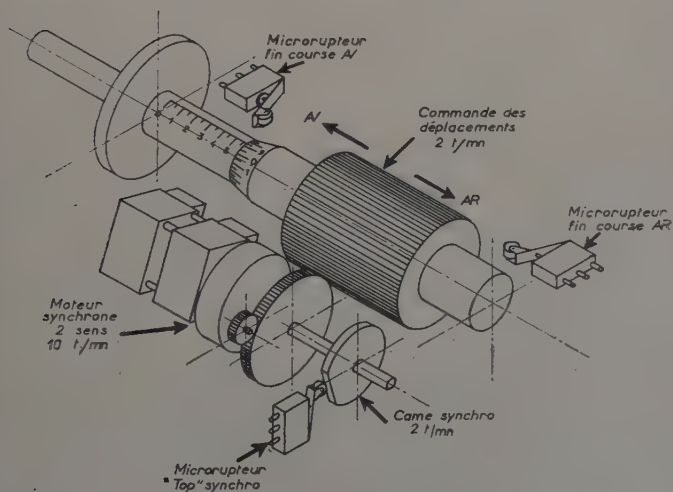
Vue schématique des différentes pièces du moteur du monochromateur.
